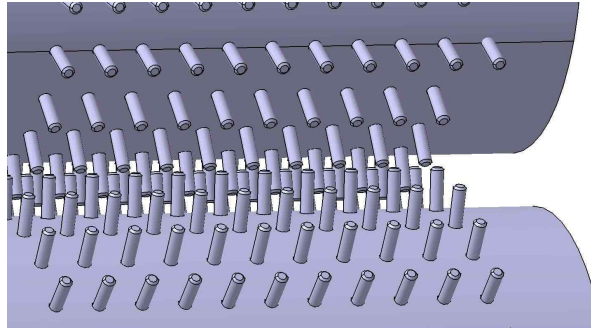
Walzenpaar mit Positiv-Werkzeugelementen - Detailansicht
